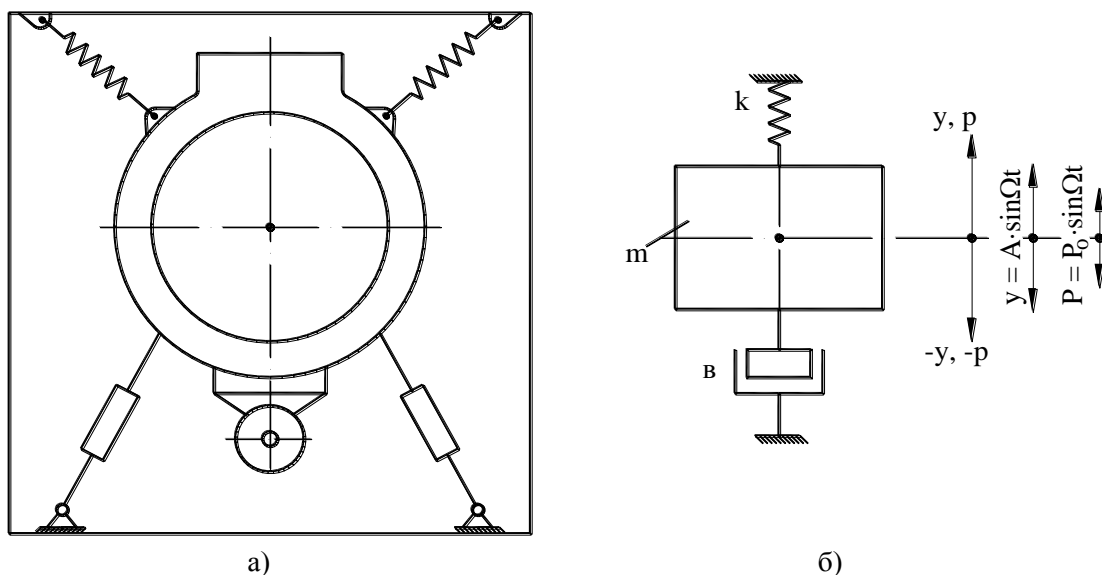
Схема пружної підвіски барабана: а – конструктивна схема; б – розрахункова схема.
